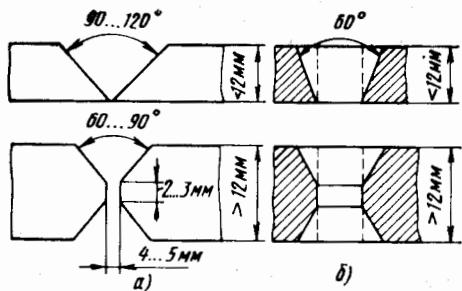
Подготовка трещины и отверстия к сварке
